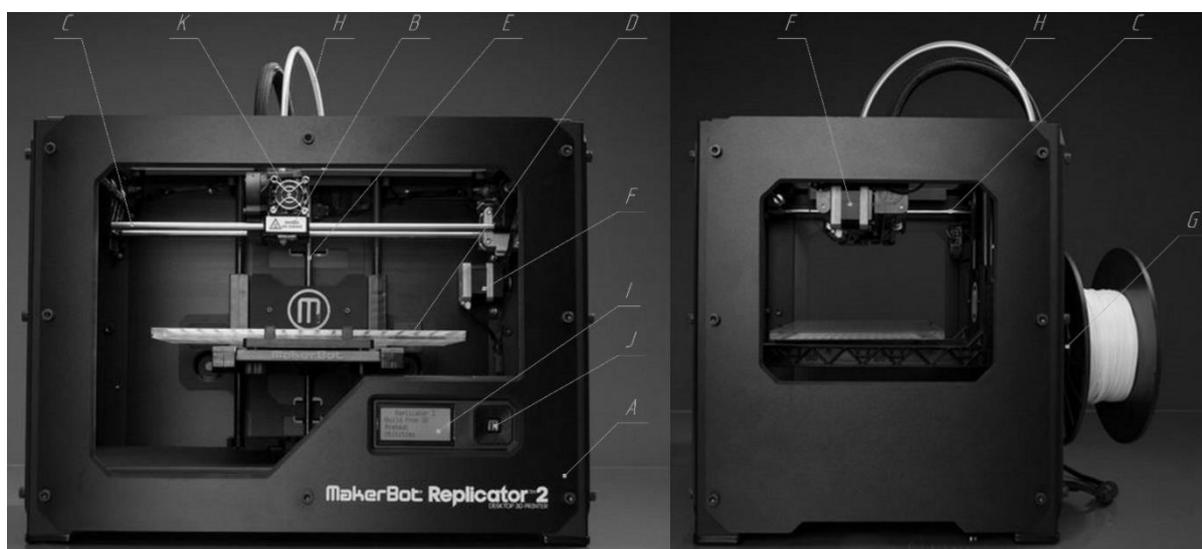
Внешний вид настольного 3-D принтера MakerBot Replicator 2
